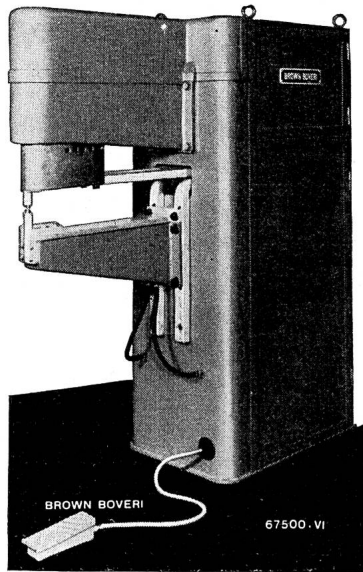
Vollautomatische Schneltpunkt-Schweissmaschine Typ PD 3 mit Spezial-Druckluftantrieb. Maximale Schweissleistung 60 kVA bei 600 mm fester Ausladung, Punktfrequenz bis 120 Schweisspunkte pro Minute oder Einzelpunktschweissung. Verschweissbare Blechdicken 0,3+0,3 bis 6+6 mm Stahl. Kleinste Schweisszeit 0,02 Sekunden bis 3 Sekunden. Eingebaute Schlagdämpfung zur Schonung der Elektrodenspitzen und Verhütung störenden Arbeitslärms. Ausrüstung der Maschine mit Röhren- oder Synchronschaltersteuerung. Diese Maschine hat auf seiten der französischen Automobilindustrie grösstes Interesse gefunden und bereits zur Bestellung einer ersten Serie geführt.
